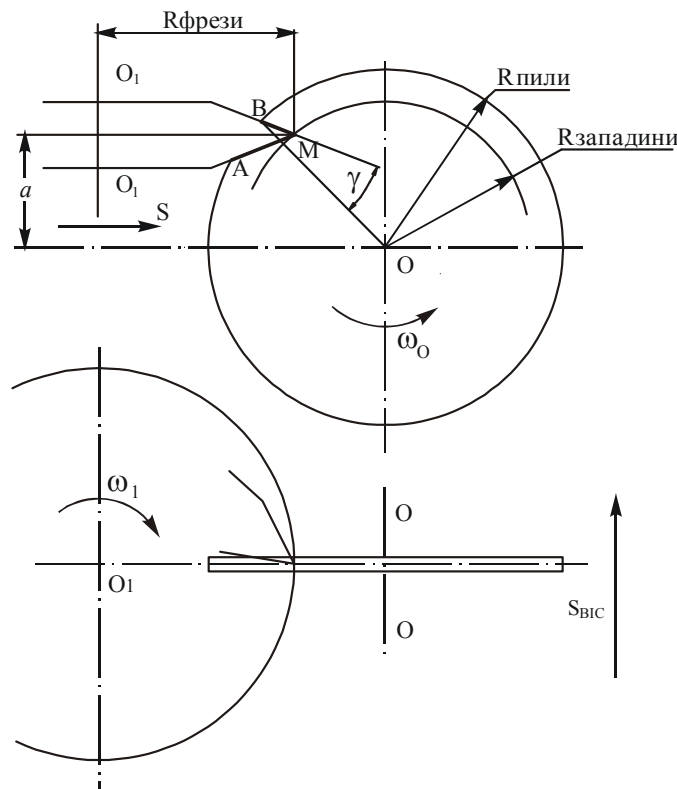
Схема установки інструменту відносно заготовки: де a – зсув осей обкатної фрези і заготовки; $R_{пили}$ – радіус заготовки (пили); $R_{западини}$ – радіус западини оброблюваного зуба; γ – передній кут заготовки (пили); S – подача обкатної фрези; $S_{вс}$ – осьова подача заготовки
